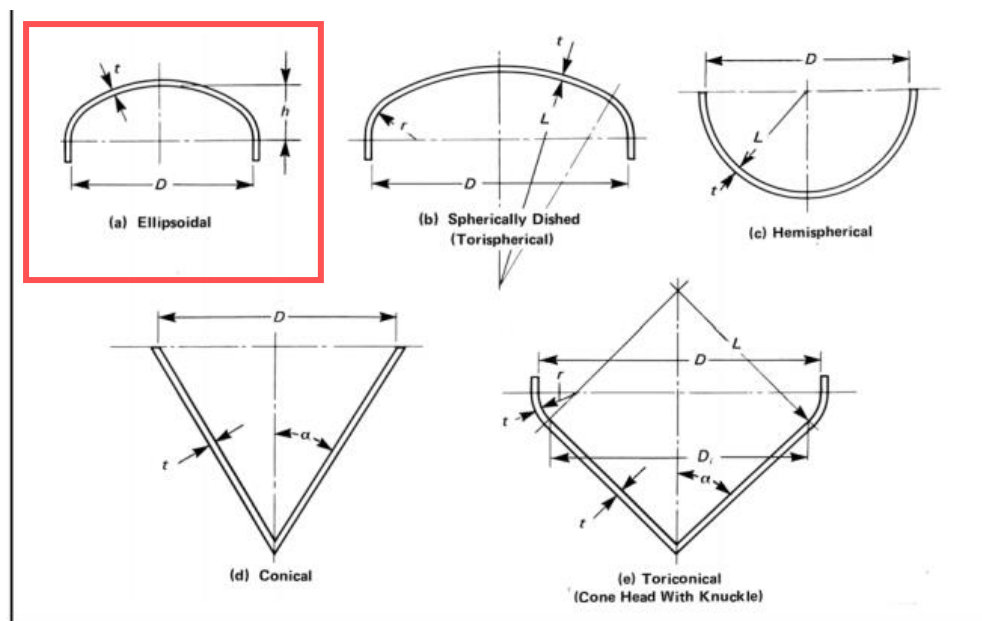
Dimensiones principales de cabezas típicas. Fuente: (ASME, ASME Boiler and Pressure Vessel Code An International Code: SECTION VIII, DIVISION 1, Rules for Construction of Pressure Vessels, 2019, pág. 378).
